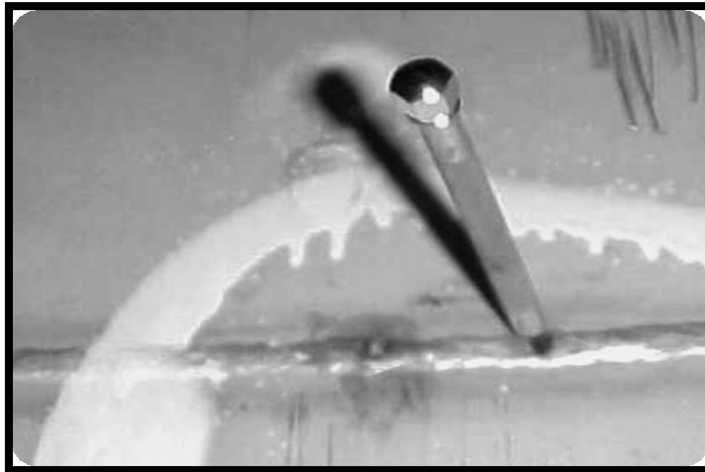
Ampliación de un cordón de soldadura con inicios de corrosión intergranular
